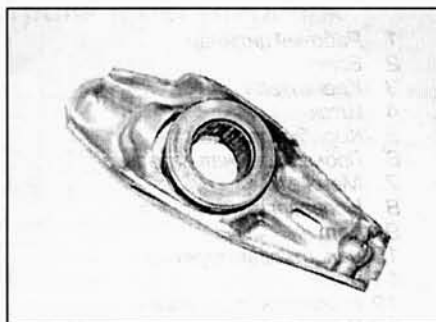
,б. Рычаг выключения сцепления и выжимной подшипник (коробки передач 012)
